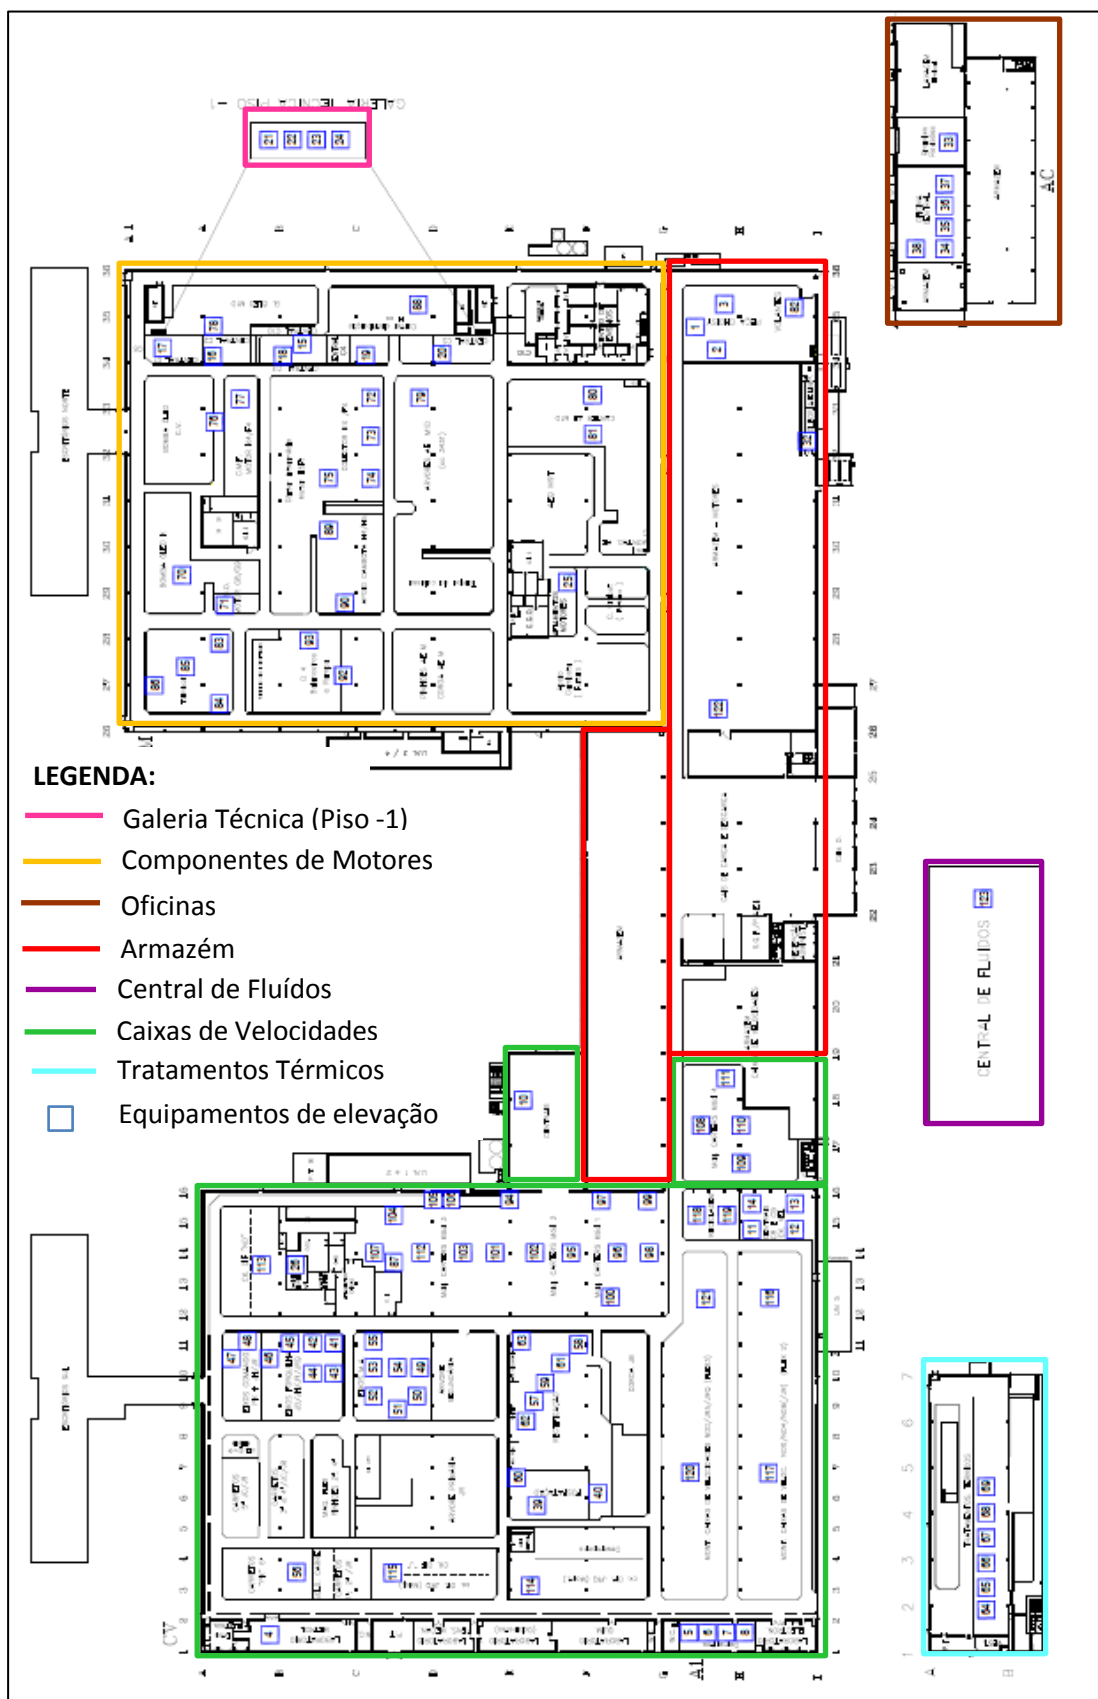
Exemplo da planta de localização dos equipamentos de elevação de carga na fábrica
